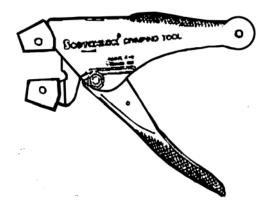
Пресс-клещи E-9BM (положение губок для работы с парными соединителями)
